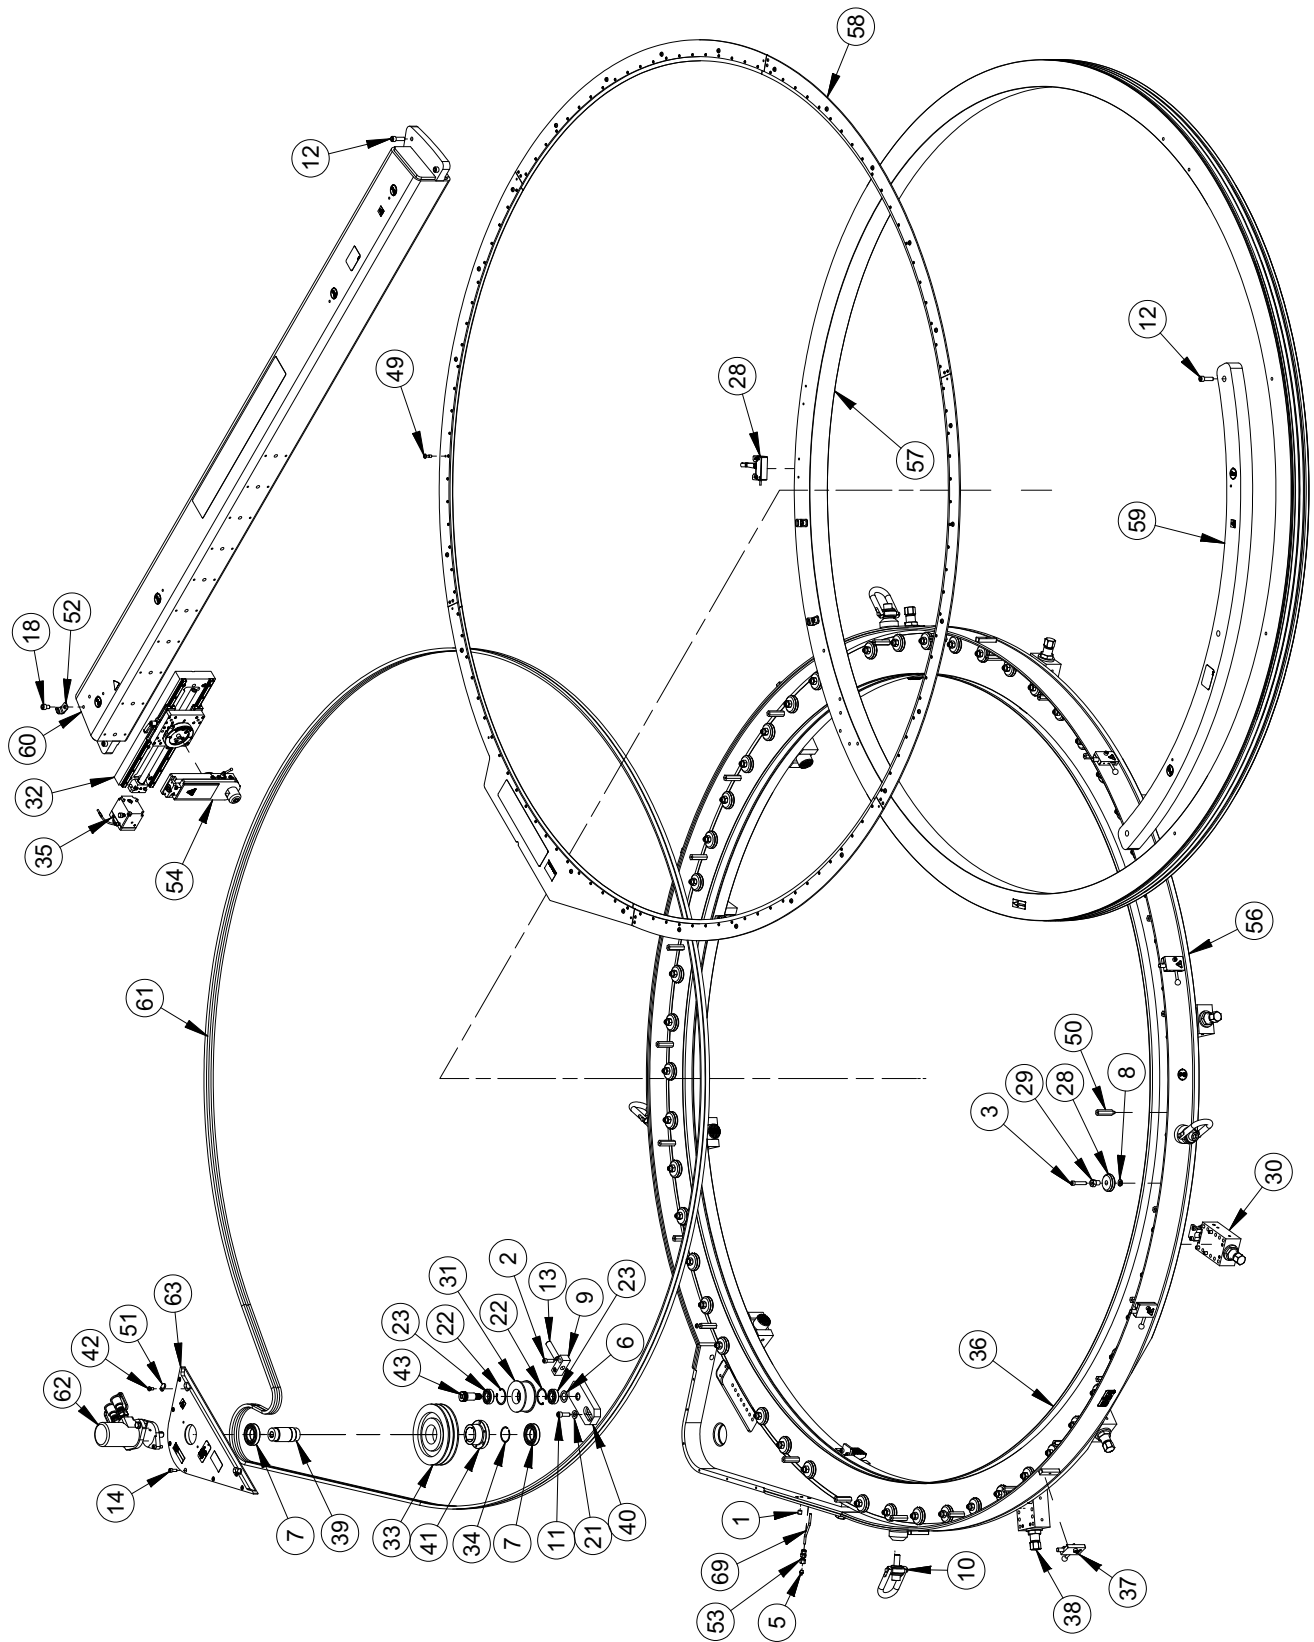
CONJUNTO 1 DE ODF110 SPEED FACER (N/P 7639-S2)
